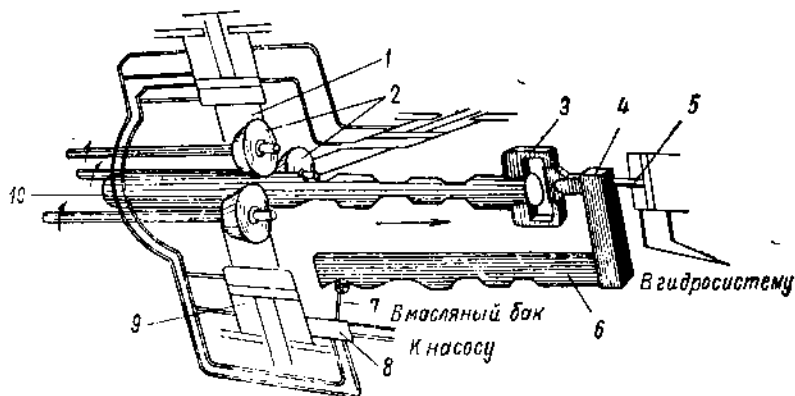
Схема прокатки изделий периодического профиля в стане с тремя коническими валками
